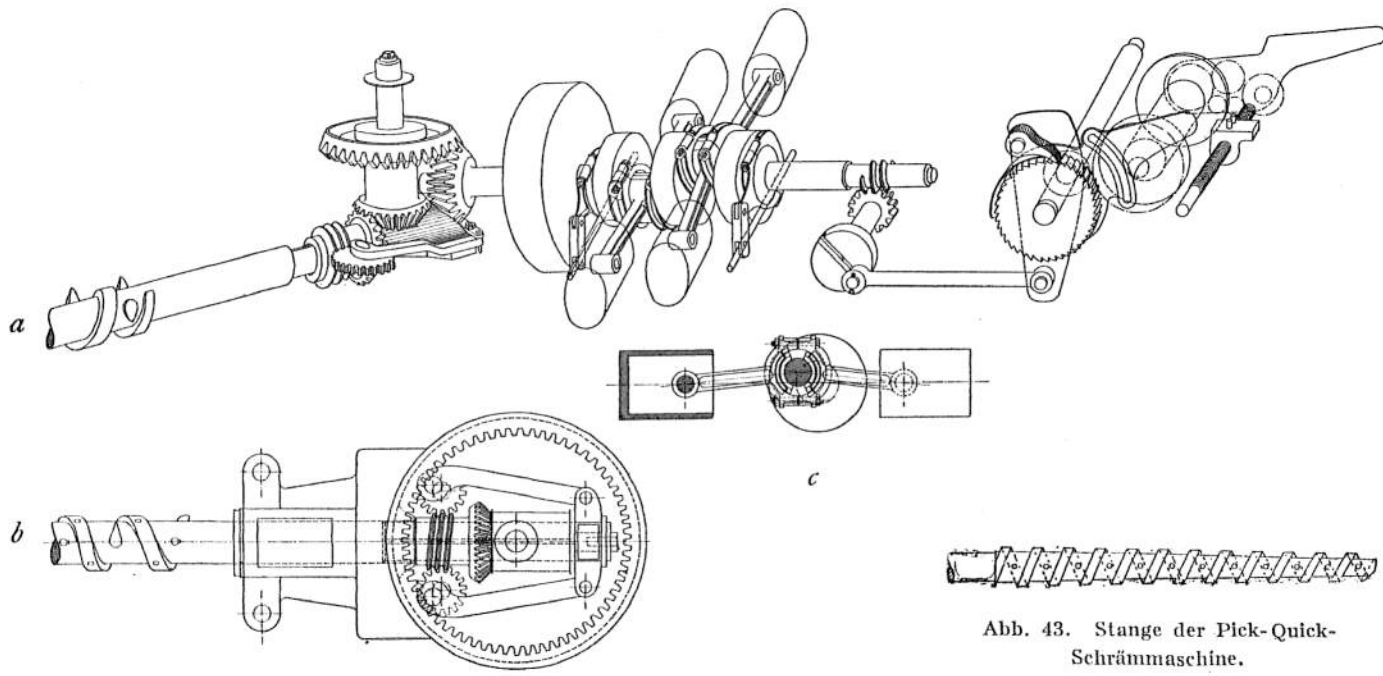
Stange der Pick-Quick-Schrämmaschine.
